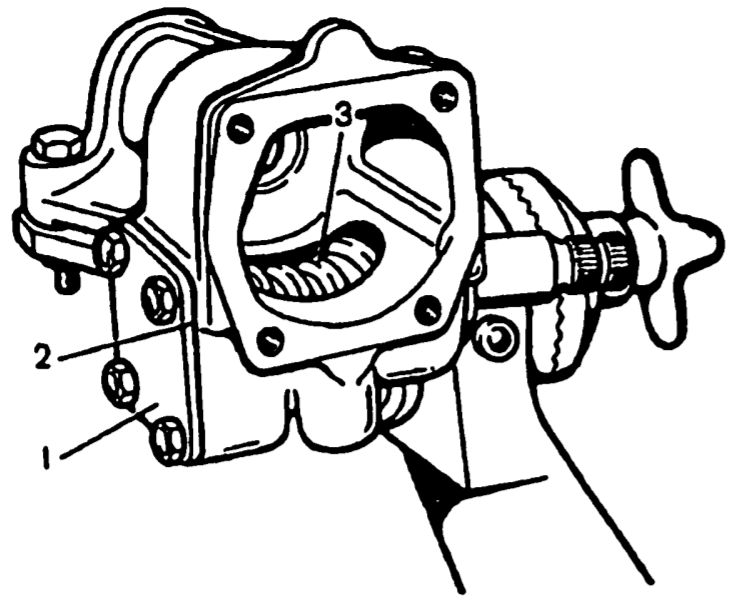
Установка червяка рулевого механизма: 1 - крышка подшипника; 2 - регулировочные прокладки; 3 - червяк
